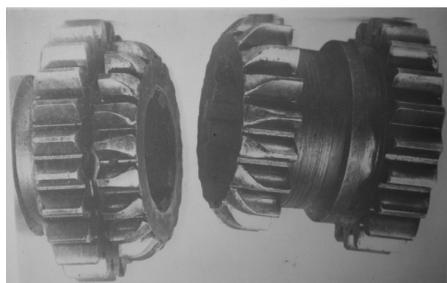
Торцевой износ шестерён коробки передач; $\times 1/8$
